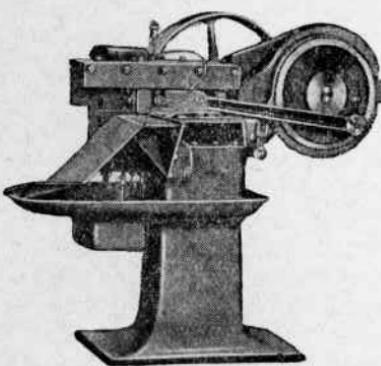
Резьбонакатный станок Ватербюри-Фаррел для накатывания очень крупных резьб.
